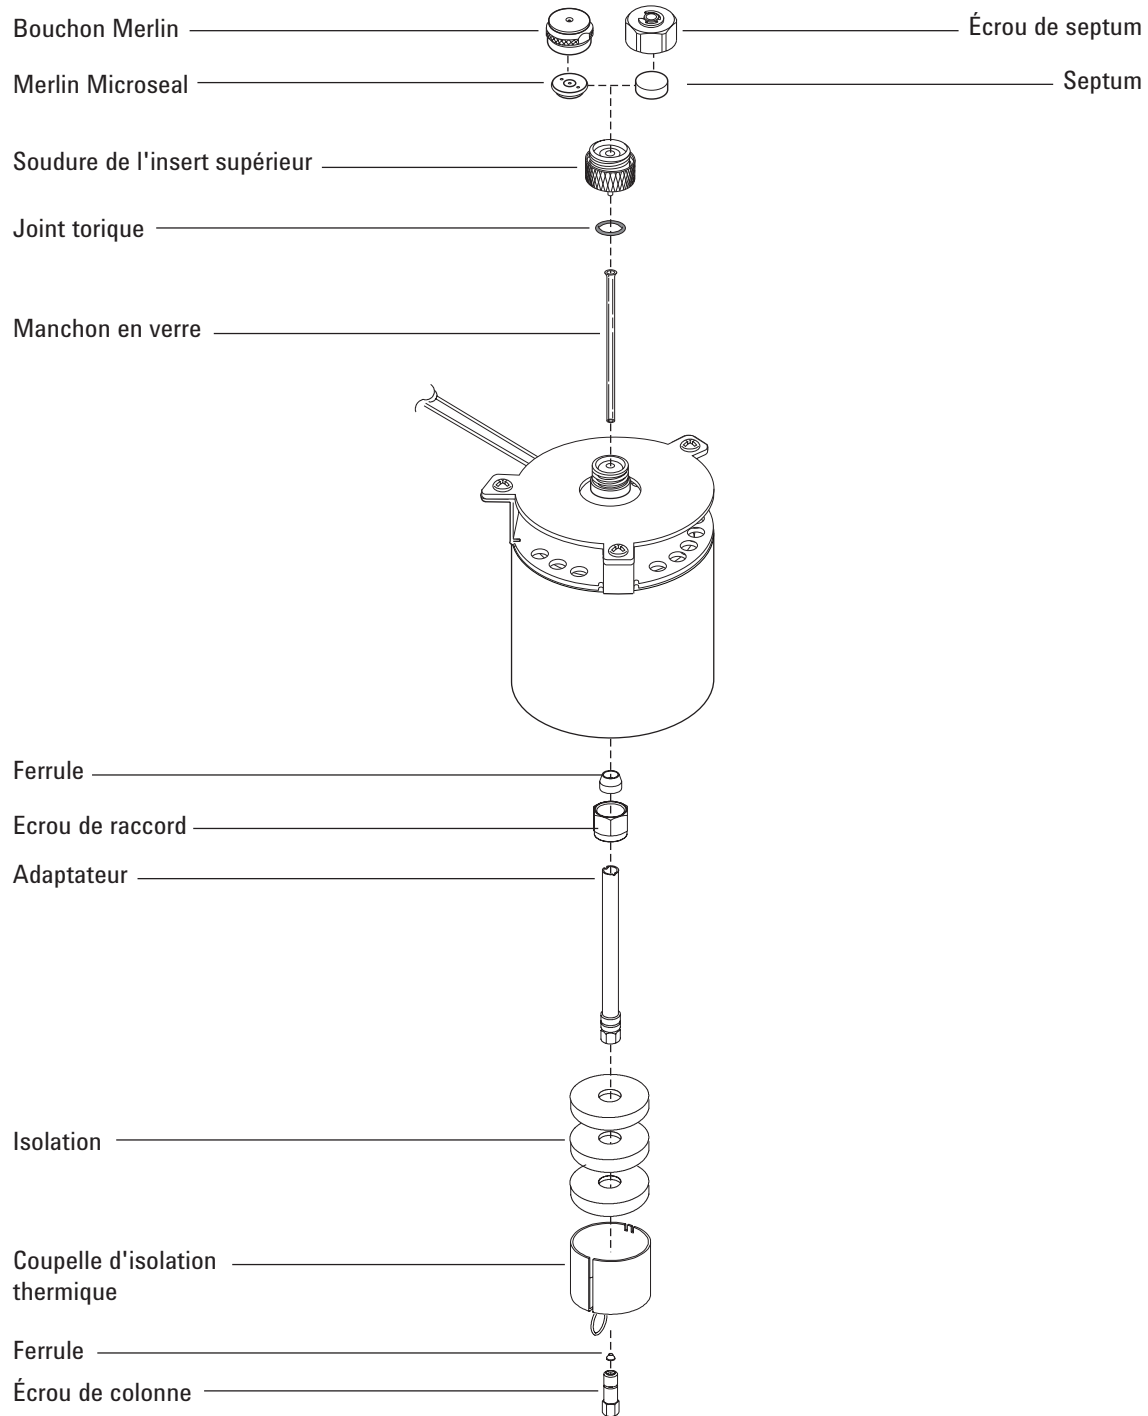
Vue éclatée des pièces pour injecteur rempli purgé
